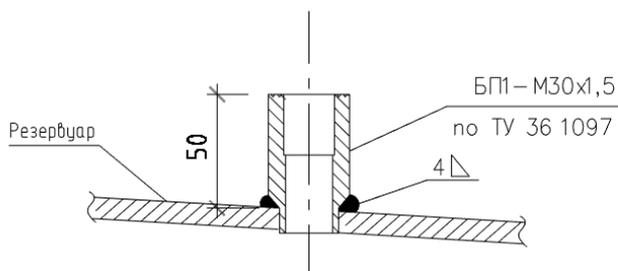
Эскиз бобышки для установки извещателя теплового пожарного
